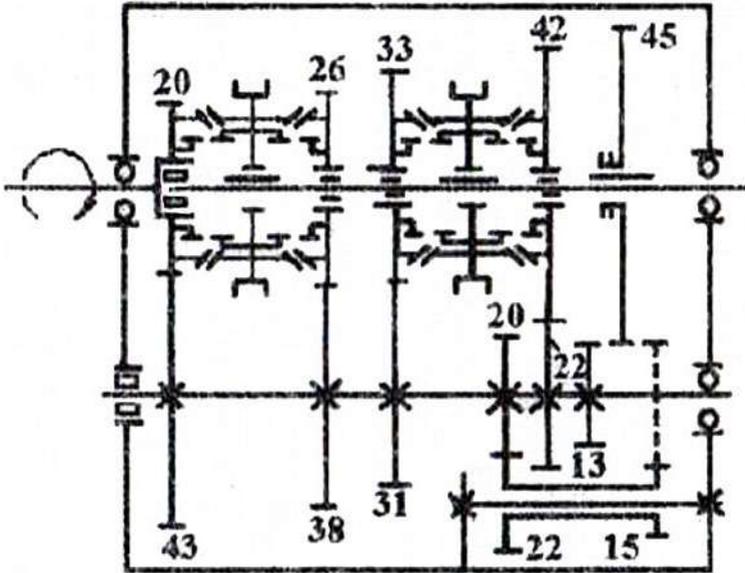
Кінематична схема коробки передач ЗІЛ-130
